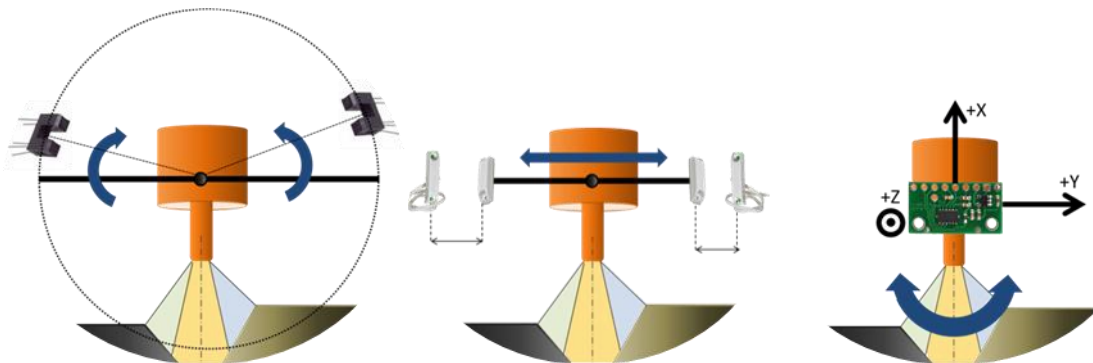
Formas de montagem mecânica na tocha de soldagem para os diferentes sensores.
